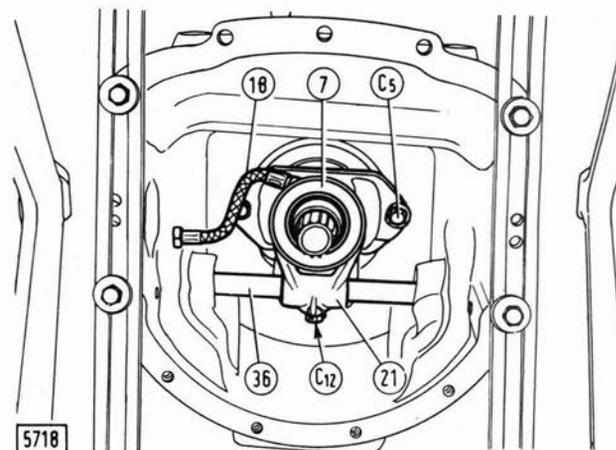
Vue avant du carter de boîte monté sur le chevalet rotatif ARR 2220.
